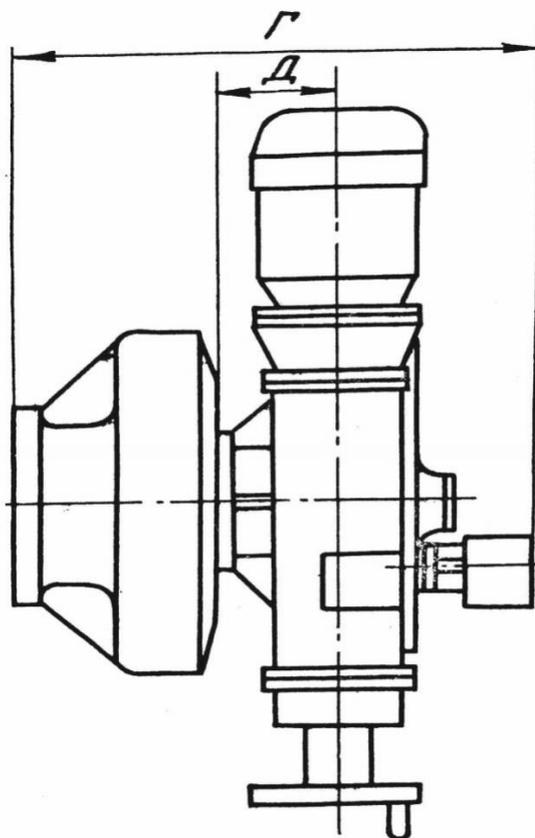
Габаритные размеры привода типа Д (остальные см. рис.4)
